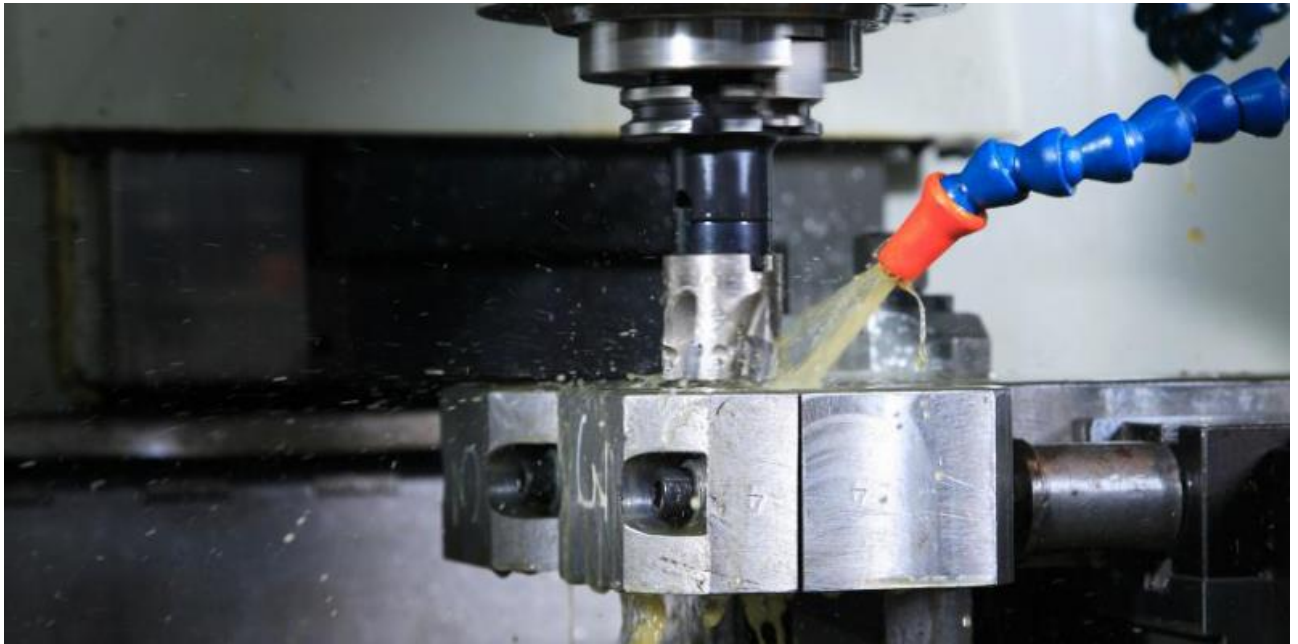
Традиційний підвід ЗОР на фрезерному верстаті з ЧПК
